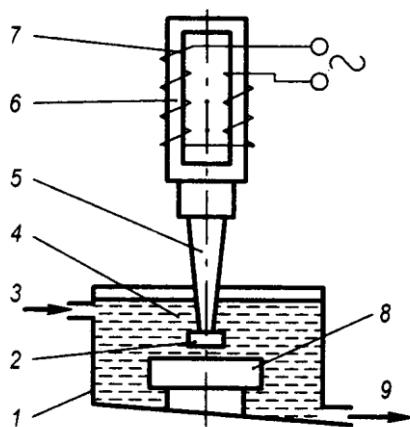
Схема ультразвукової обробки: 1 – ванна; 2 – інструмент; 3 – рух рідини від насоса; 4 – абразивна суспензія; 5 – хвилевід; 6 – осердя; 7 – обмотка; 8 – заготовка; 9 – рух рідини до насоса
